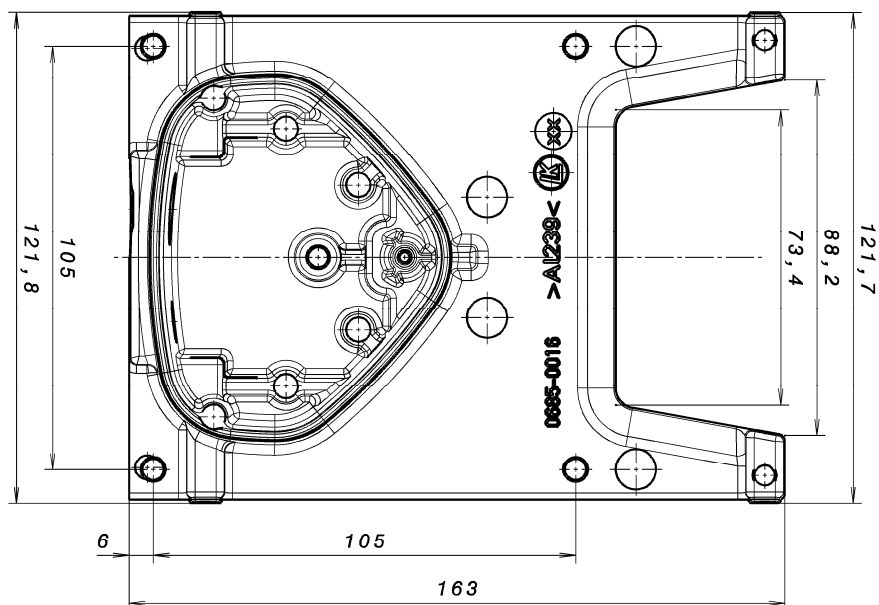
Bohrbild Standard-Wand- Adapterplatte BG B
